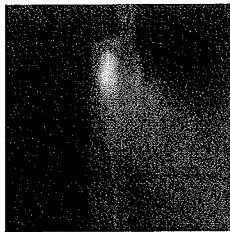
In-Prozess-Aufnahme beim Schweißen einer Bördelnaht mit einem Spalt von 0,6 mm zwischen den Blechen.
